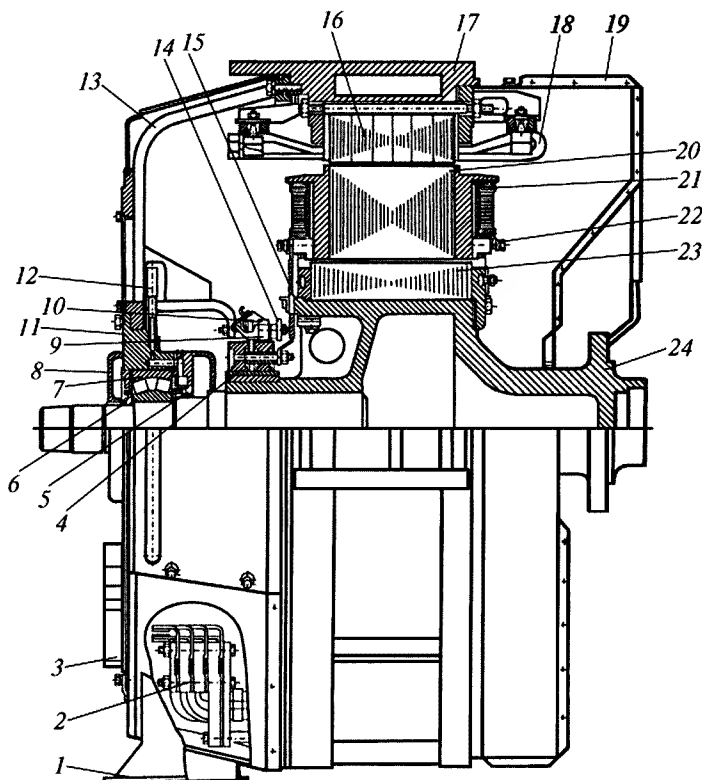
Продольный разрез синхронного тягового генератора ГСТ 2800-1000: 1 — выходной патрубок; 2 — выводы обмоток статора; 3 — клицы; 4 — контактные кольца; 5, 8 — задняя и передняя крышки подшипника; 6 — уплотнительное кольцо; 7 — роликовый подшипник; 9 — щеткодержатель; 10 — щетка; 11 — ступица; 12 — смазочная трубка с масленкой; 13 — подшипниковый щит; 14 — траверса; 15 — соединительная шина; 16, 18 — сердечник и обмотка статора; 17 — корпус; 19 — кожух; 20, 21 — сердечник и катушка полюса; 22 — межполюсная шина; 23 — магнитопровод; 24 — корпус ротора
